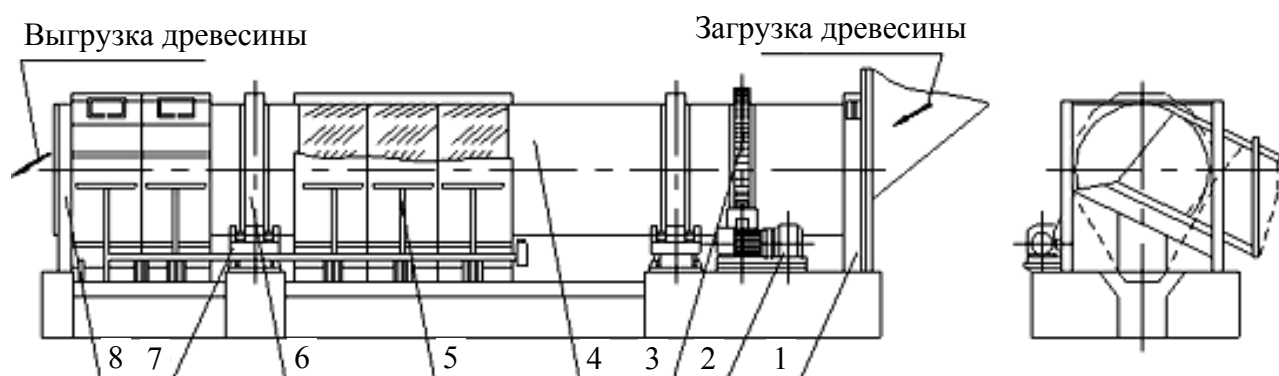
Односекционный корообдирочный барабан [27]:
